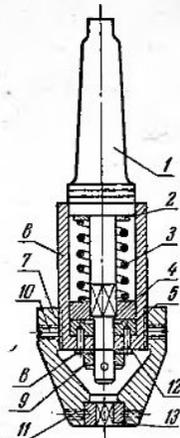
Динамометрический патрон к сверльному станку для нарезания резьбы метчиками:
